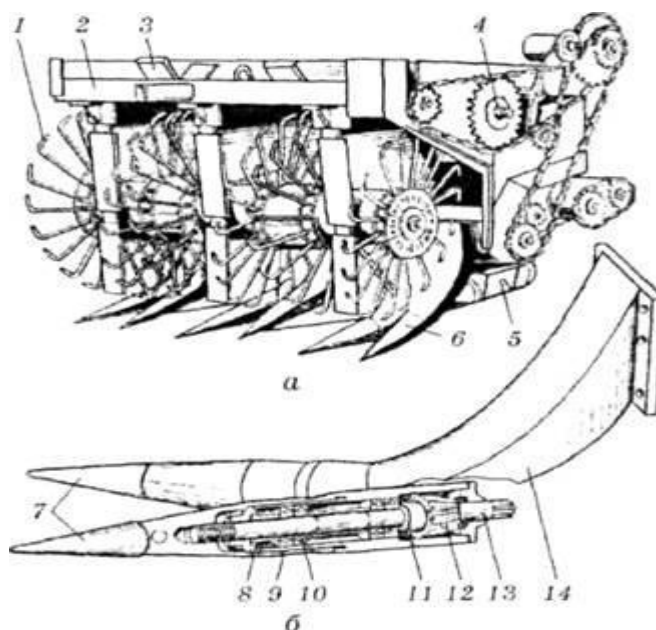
Викопувальний пристрій коренезбиральної машини МКК-6-02:
